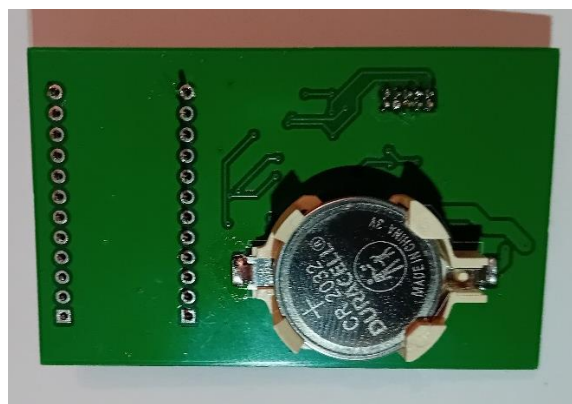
Parte inferior BLE\_PCB\_V1 con componentes soldados
